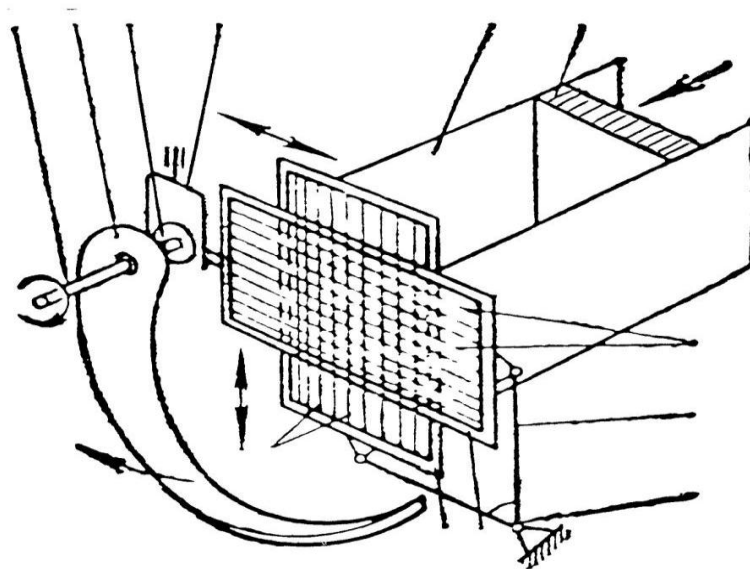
Шпигорізка. Принципова схема різального вузла: 1 – приводний вал; 2 – серпоподібний ніж; 3 – ексцентрик; 4 – вилка; 5 – ножові рамки; 6 – пластинчасті ножі; 7 – вісь; 8 – кутовий важіль; 9 – штовхальник; 10 – короб живлення.
